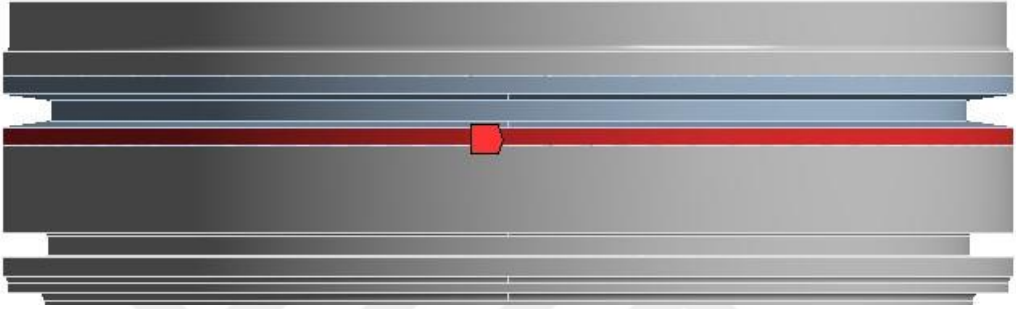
Piston üst yüzeyi ile alfin bölgesi arasında kalan bölge (topland)
